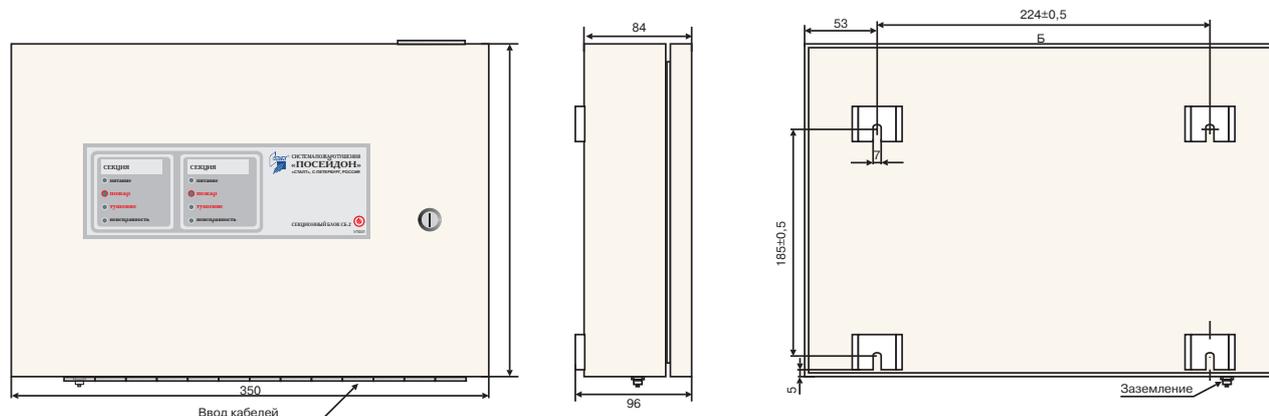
Габаритный чертеж СБ-1, СБ-2.
